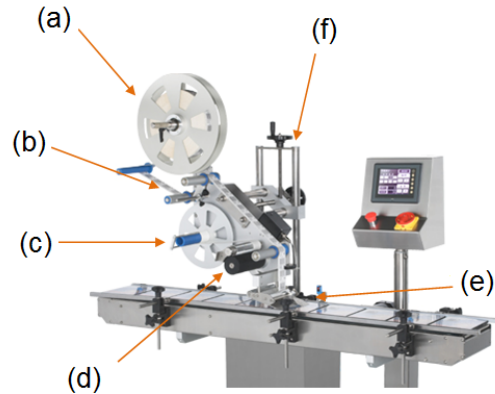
Descripción de la parte mecánica de la máquina etiquetadora [9]. (a) Contenedor de cinta. (b) Sistema de ejes mecánicos. (c) Receptor de cinta. (d) Rodillos de arrastre. (e) Cuña. (f) Sistema de posicionamiento
